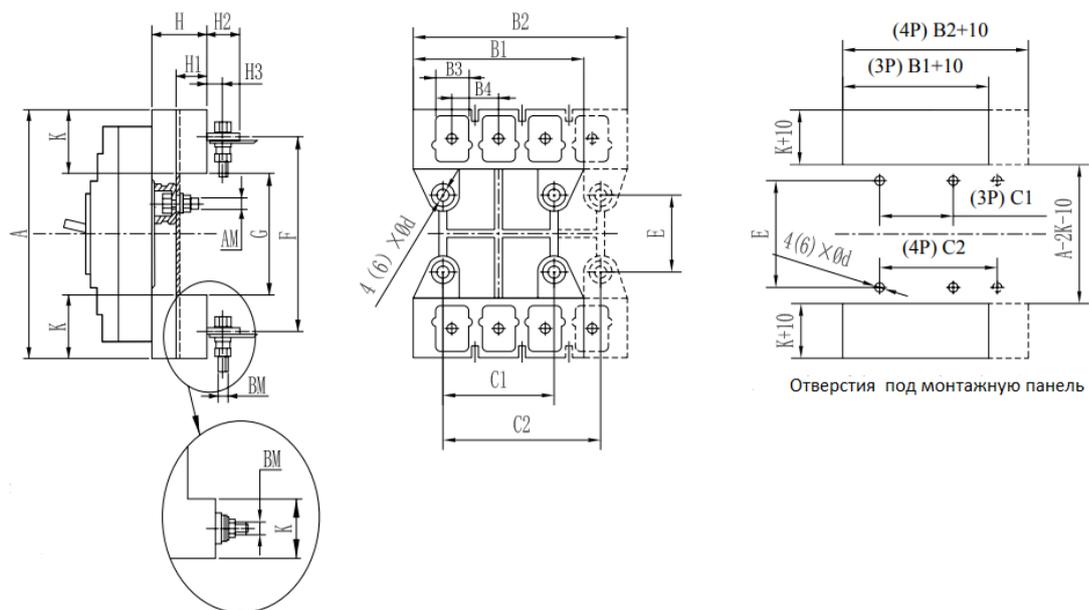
Габаритные и установочные размеры втычного исполнения заднего присоединения
